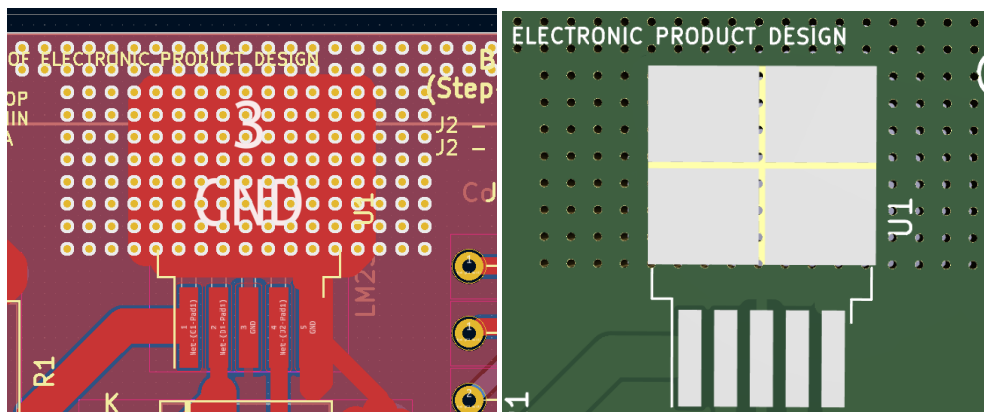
ผลการแบบ PCB (Bottom Layer)
